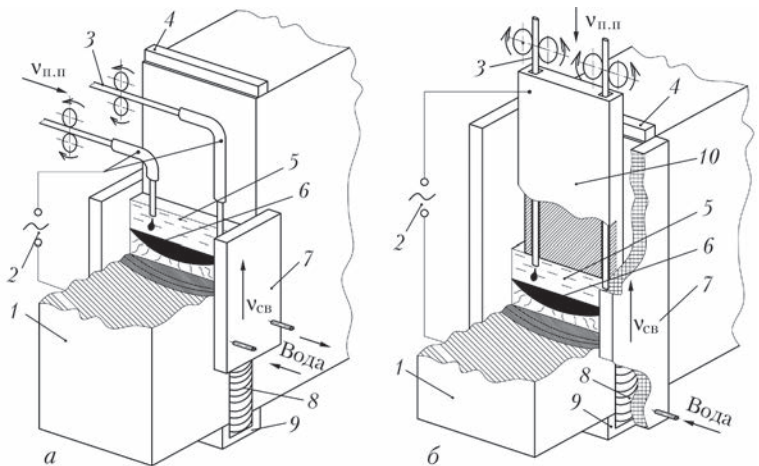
Схемы ЭШС проволочными электродами (а) и плавящимся мундштуком (б): 1 — свариваемые изделия; 2 — источник питания; 3 — сварочная проволока; 4 — выводная планка; 5 — шлаковая ванна; 6 — металлическая ванна; 7 — водоохлаждаемая формирующая планка (ползун); 8 — сварной шов; 9 — входной карман; 10 — мундштук
